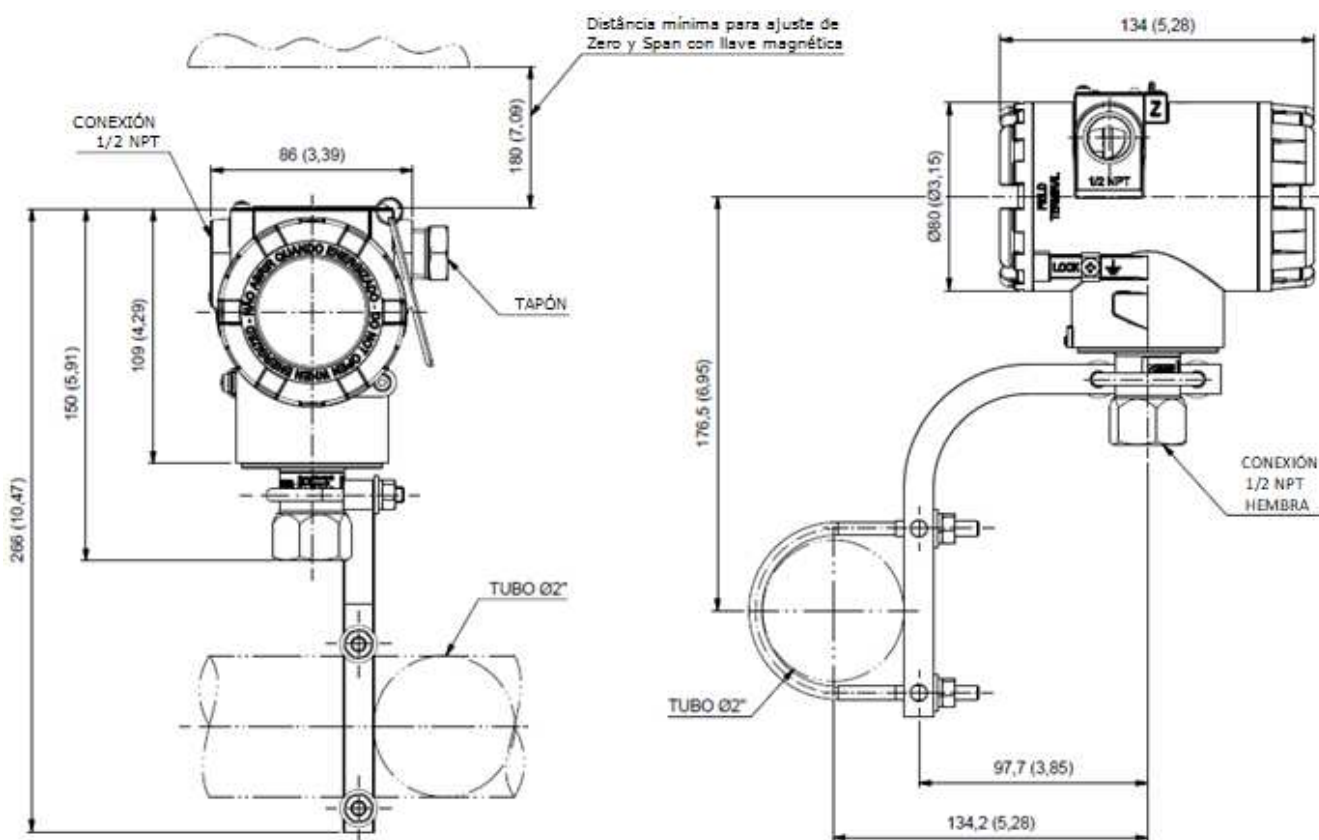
Diseño dimensional y esquema de montaje del VPT11-P.
